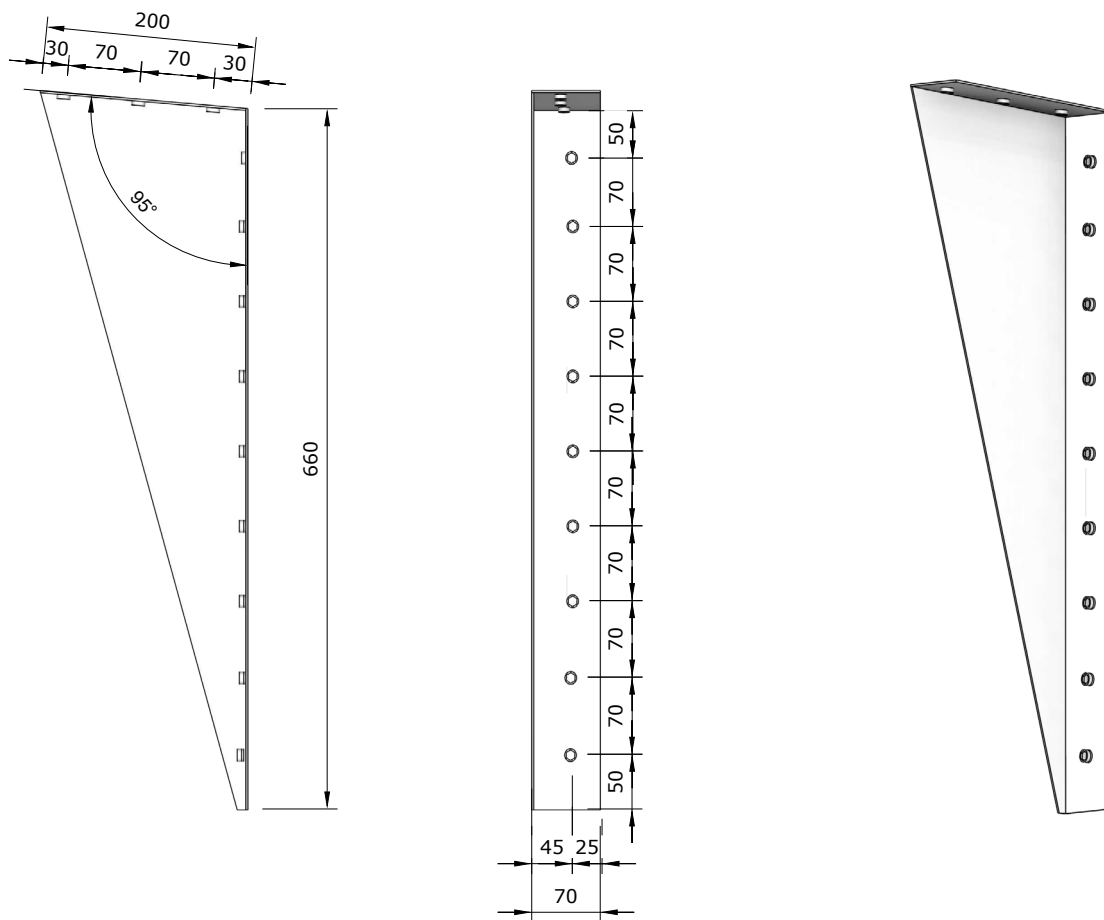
Ansichten des Stützbleches mit der Vermessung der Befestigung, Masse in mm.
